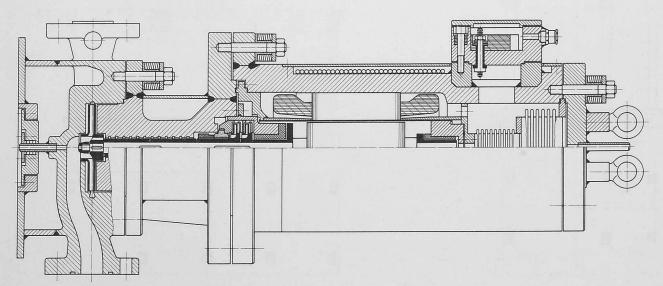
Pumpe mit Spaltrohrmotor für hohe statische Drücke, mit Heiz- und Kühlvorrichtung für Pumpengehäuse und Motor
